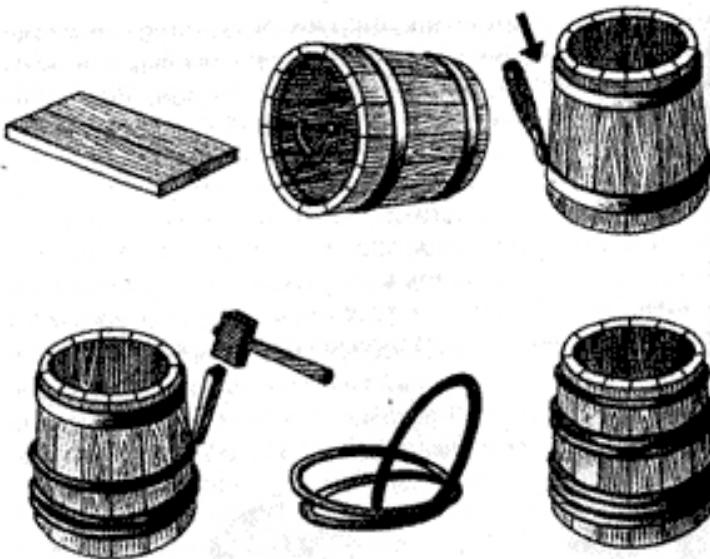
Изготовление посуды с конической боковой поверхностью (продолжение)
